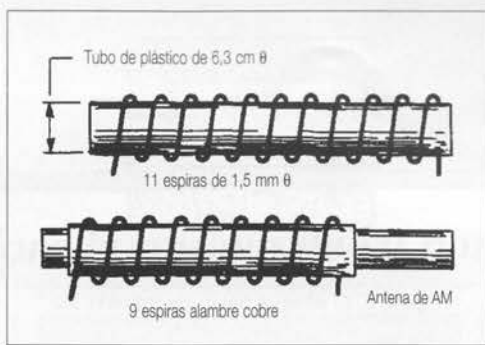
Detalles constructivos de dos alternativas de la bobina en derivación.
